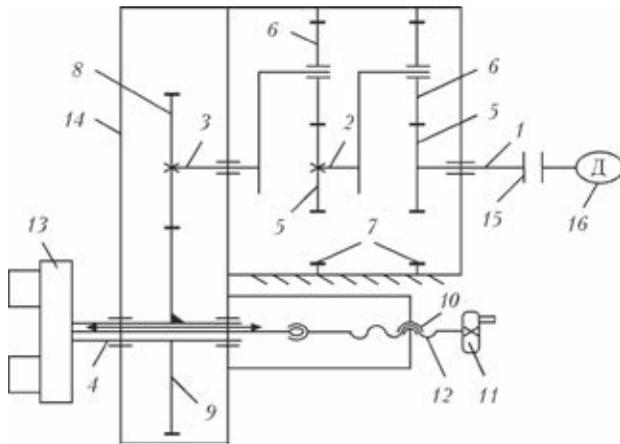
Кинематическая схема торцевателей ТРЦ 38 У3.1 и ТРЦ 76 У3.1: 1–4 — валы кинематических звеньев; 5–9 — шестерни кинематических звеньев; 10 — гайка; 11 — маховичок; 12 — винт ходовой; 13 — планшайба; 14 — корпус; 15 — муфта; 16 — пневмодвигатель
